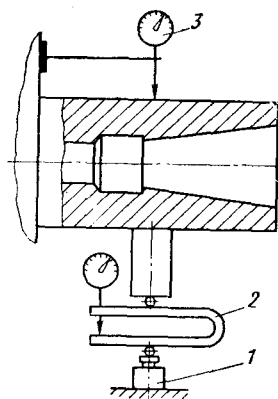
Схема проверки величины радиального зазора в шпинделях с подшипниками скольжения
